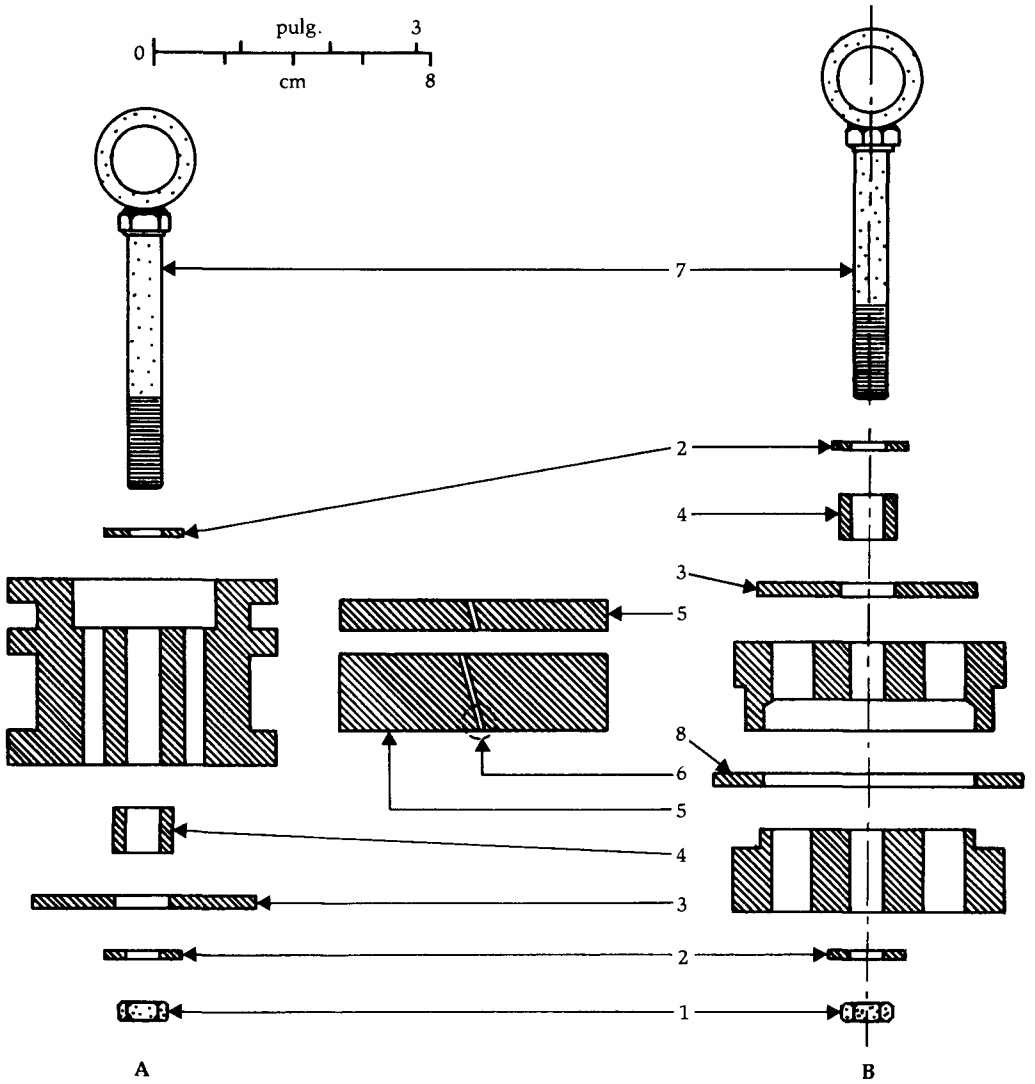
(A) Pistón y (B) válvula de pedal original: (1) tuerca hexagonal; (2) arandela simple; (3) casquillo de válvula plástica; (4) guía deslizante del casquillo; (5) anillo de plástico del pistón; (6) corte diagonal; (7) perno roscado con unión soldada en el lugar; y (8) cierre de caucho.
